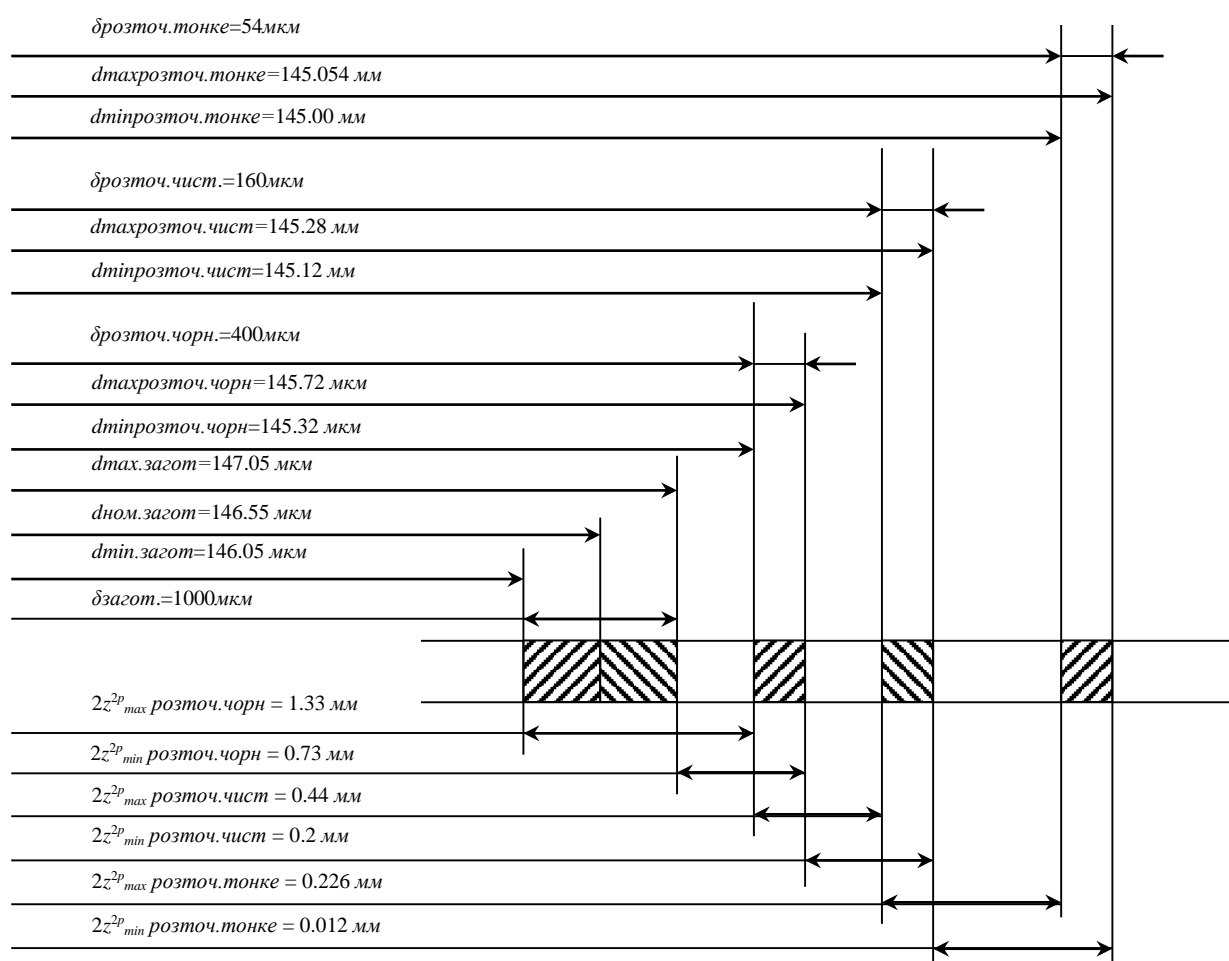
Схема розташування припусків і допусків на обробку розміру 145h8
